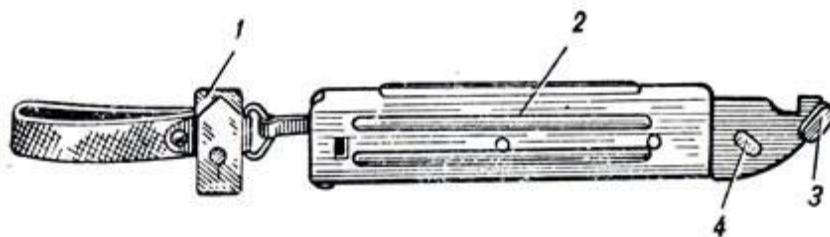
Ножны: 1 — подвеска с карабинчиками; 2 — пластмассовый корпус; 3 — упор; 4 — выступ-ось
